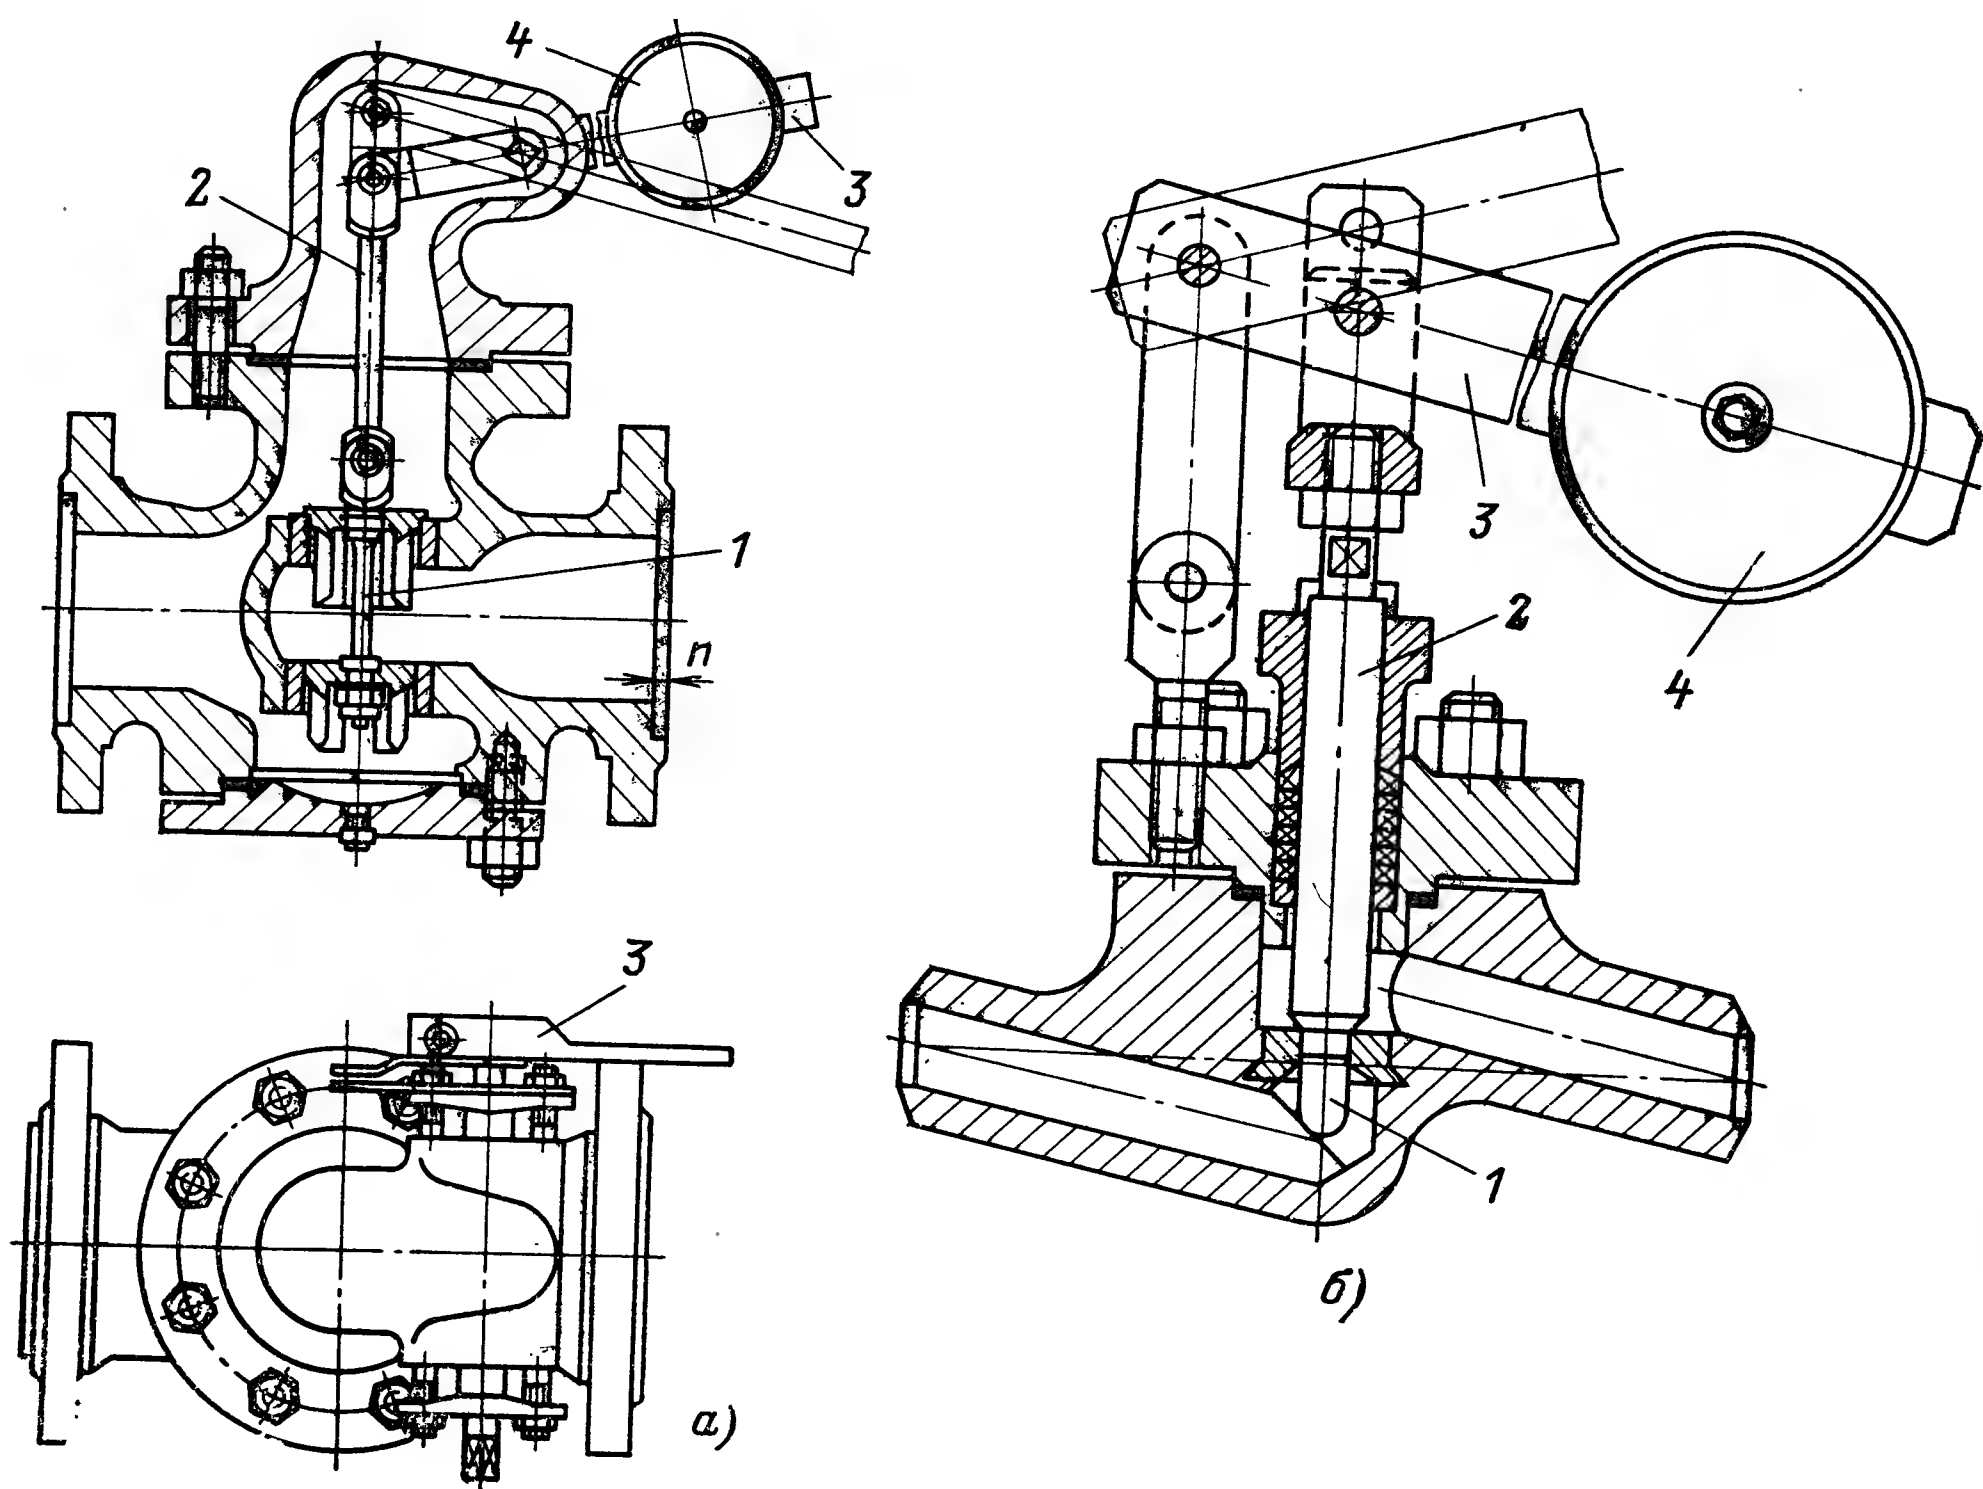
Регулирующие давление клапаны с фланцами (а) и для сварки с трубопроводом (б).
